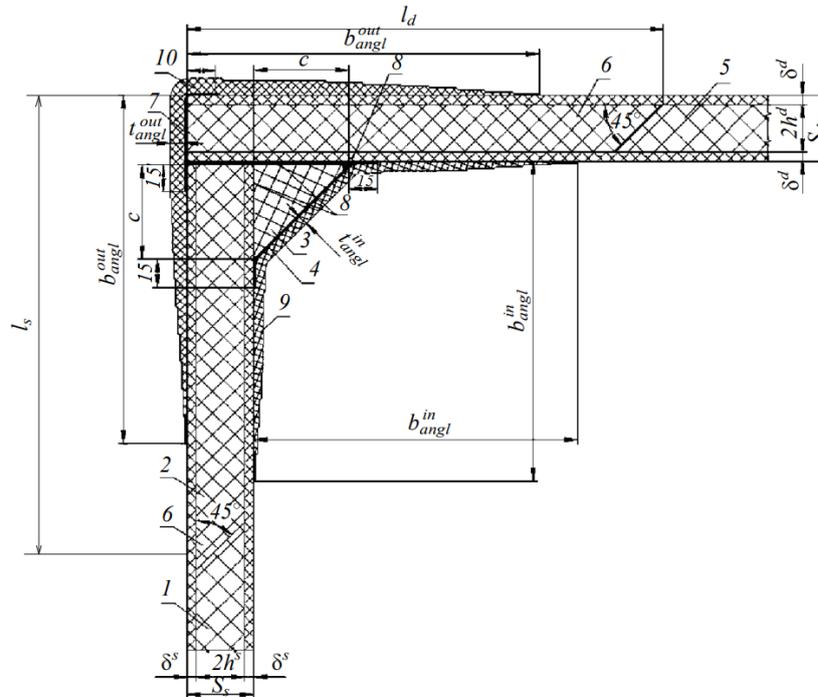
Вузол з'єднання настилу верхньої палуби і обшивки борту тришарової конструкції (Варіант А):
